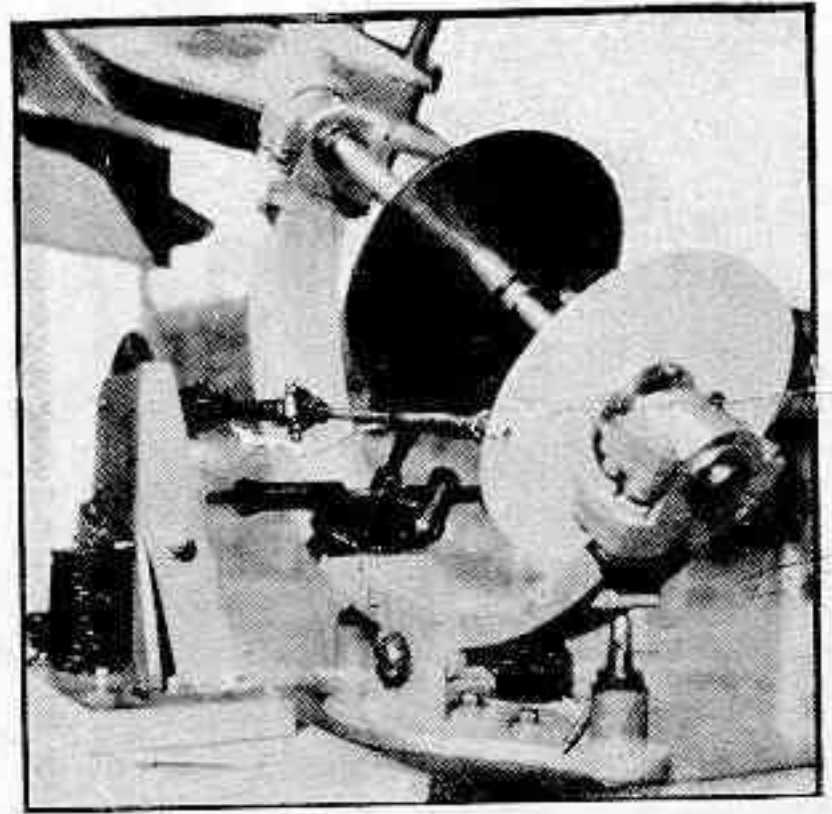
Transmisión cardánica del motor al "sin fin".
